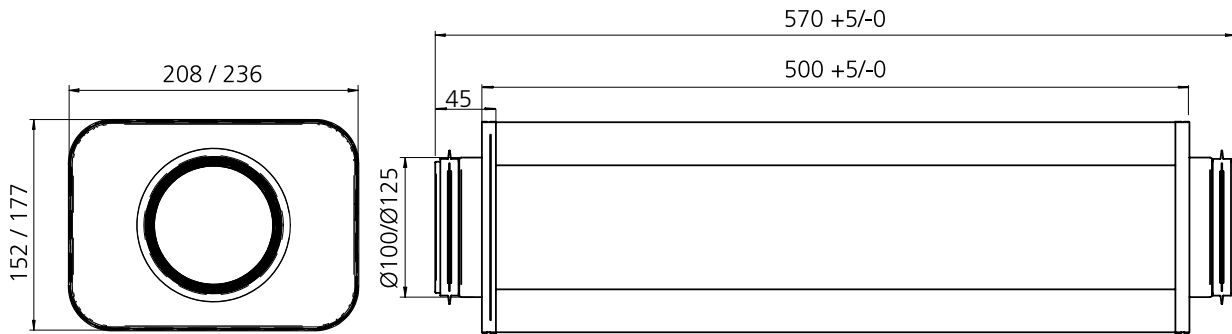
Maßzeichnung Schalldämpfer CLA Ø100-500 oder Ø125-500.
